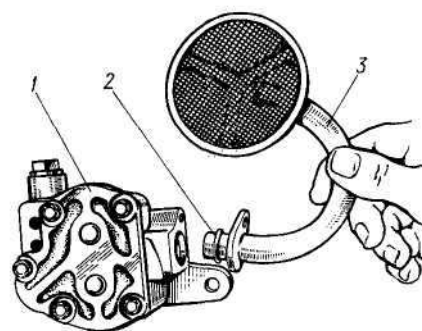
Снятие маслоприёмника и уплотнительного резинового кольца:
